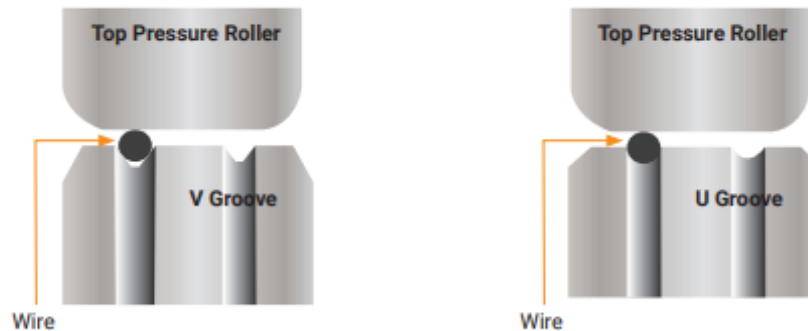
Configuração dos rolos de fio de soldadura
